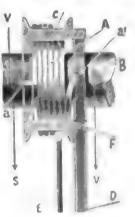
"Fixator" für Seilzug. A = Spiralfeder, $a_1 \ a_2 = Mitnehmer$, B = Welle, C = Seiltrommel, D = Handhebel, E = Drahtseil, F = Mitnehmer für Hebel D.
